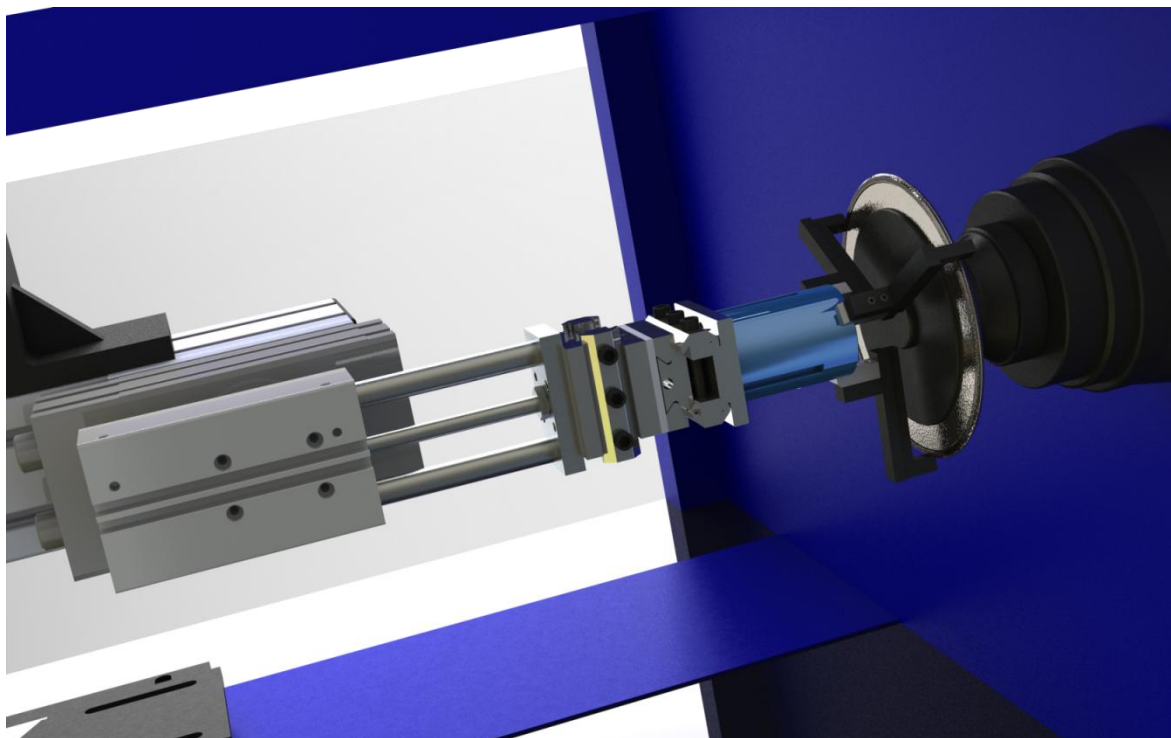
Manipulátor pred vyložením hotového tesnenia.
